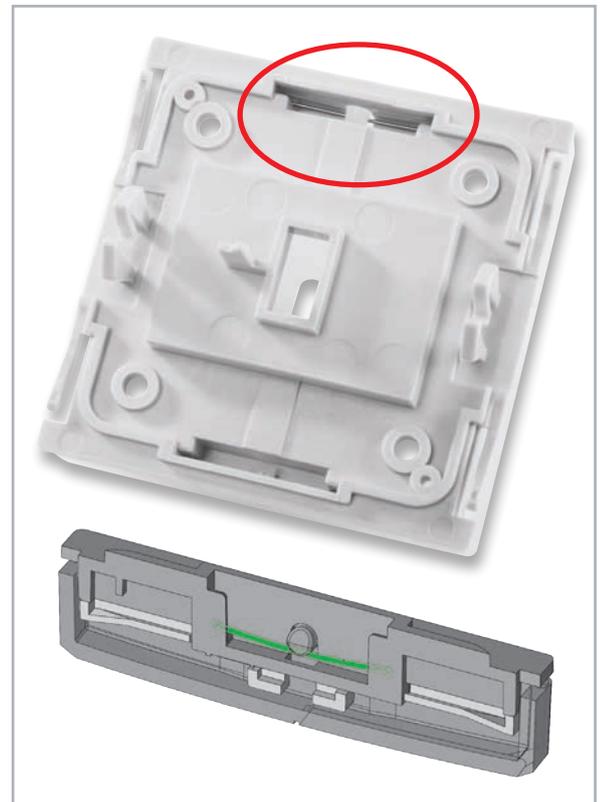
So sind die Federdrahtstücke in die Unterseite des Gehäuseteils einzusetzen.
